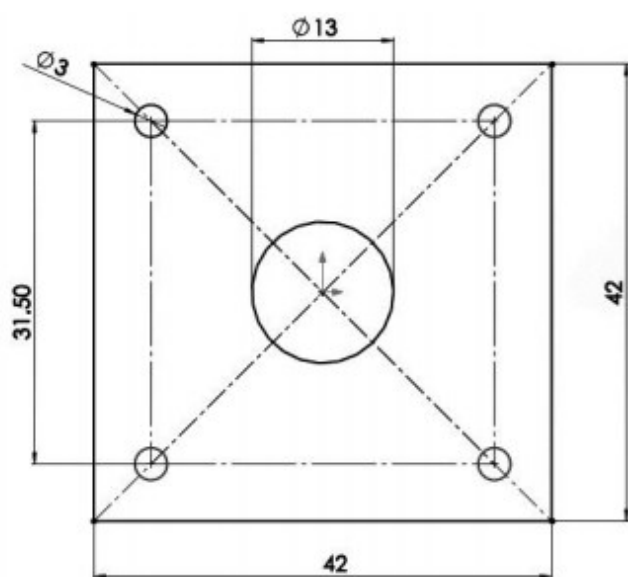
Пластина для утримання двигуна і екструдера
